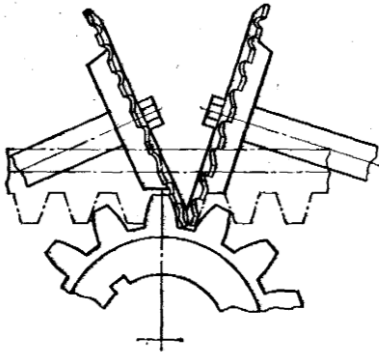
Схема фрезерування двома дисковими фрезами за методом обкатування
